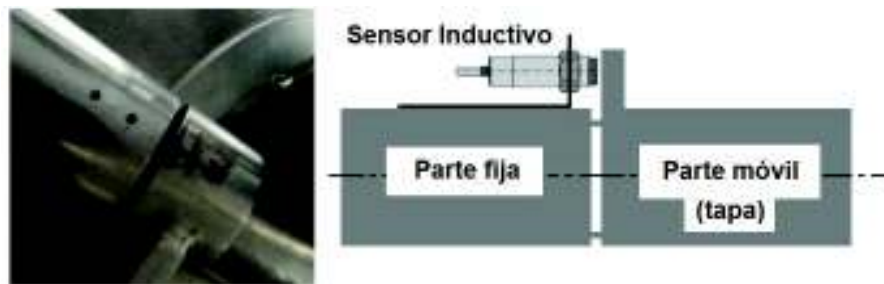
Ubicación del sensor de proximidad inductivo que indica, tapa cerrada.
